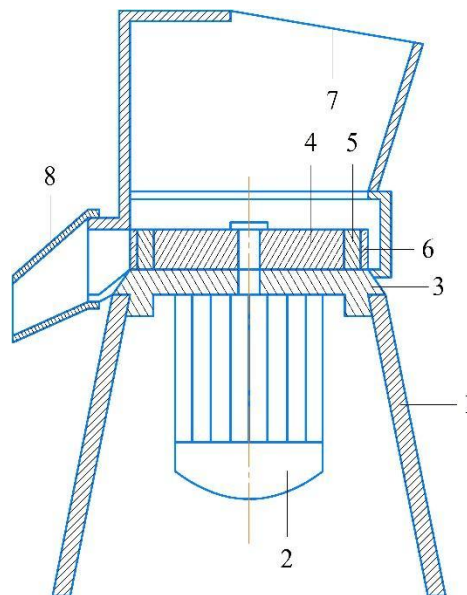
Ножовий подрібнювач: 1 – станина; 2 – фланцевий електродвигун; 3 – корпус; 4 – диск; 5 – ножі; 6 – змінна калібрувальна решітка; 7 – завантажувальна воронка; 8 – лоток.
